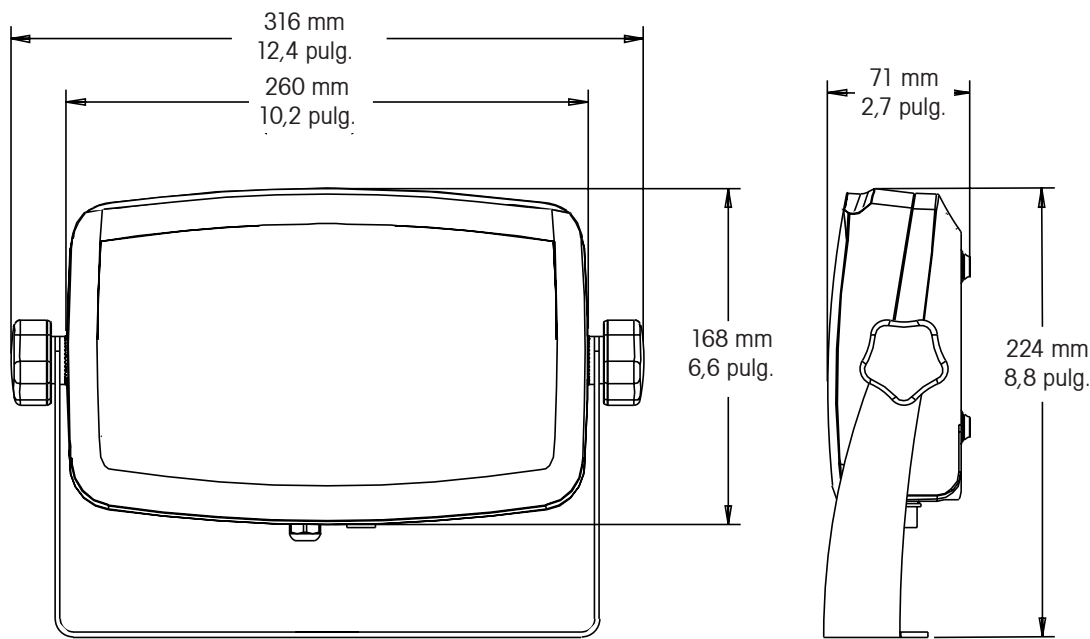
Dimensiones generales del indicador T51P sin soporte de montaje.
